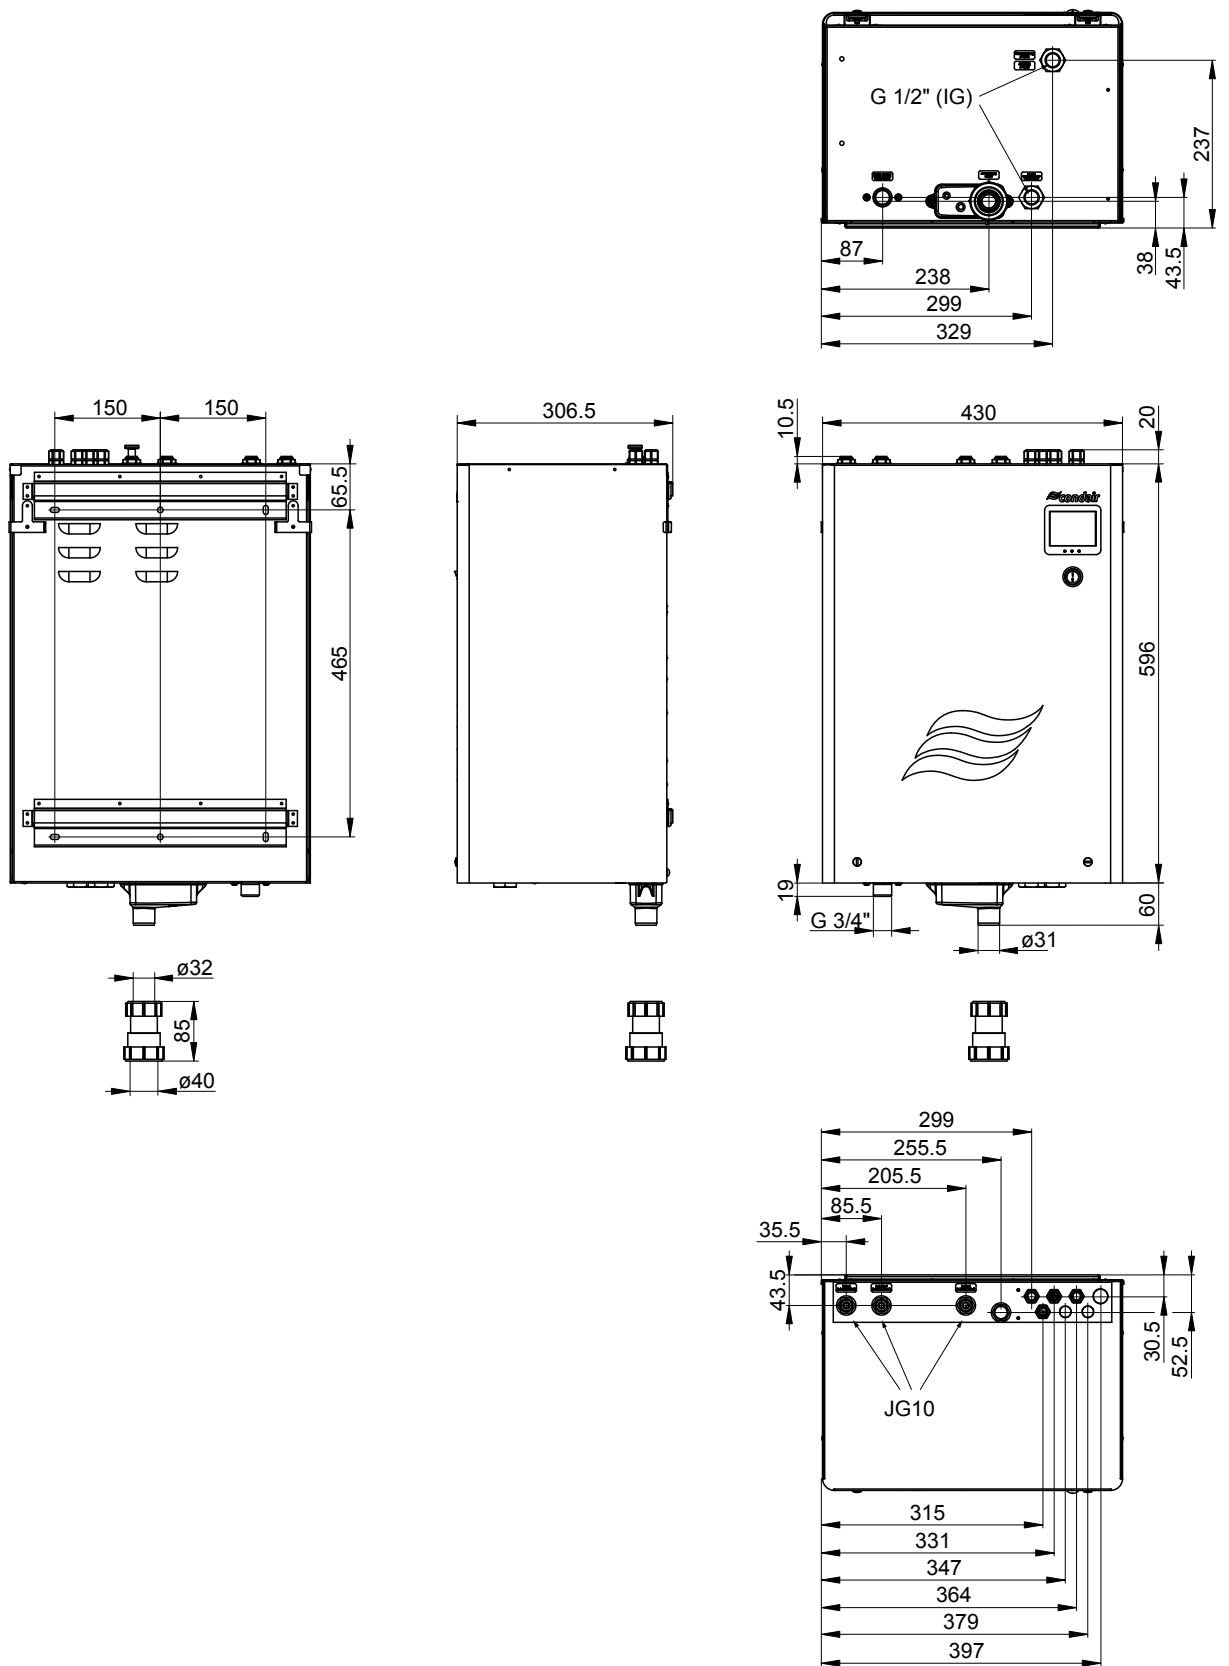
Dimensions unité hydraulique (dimensions en mm)
